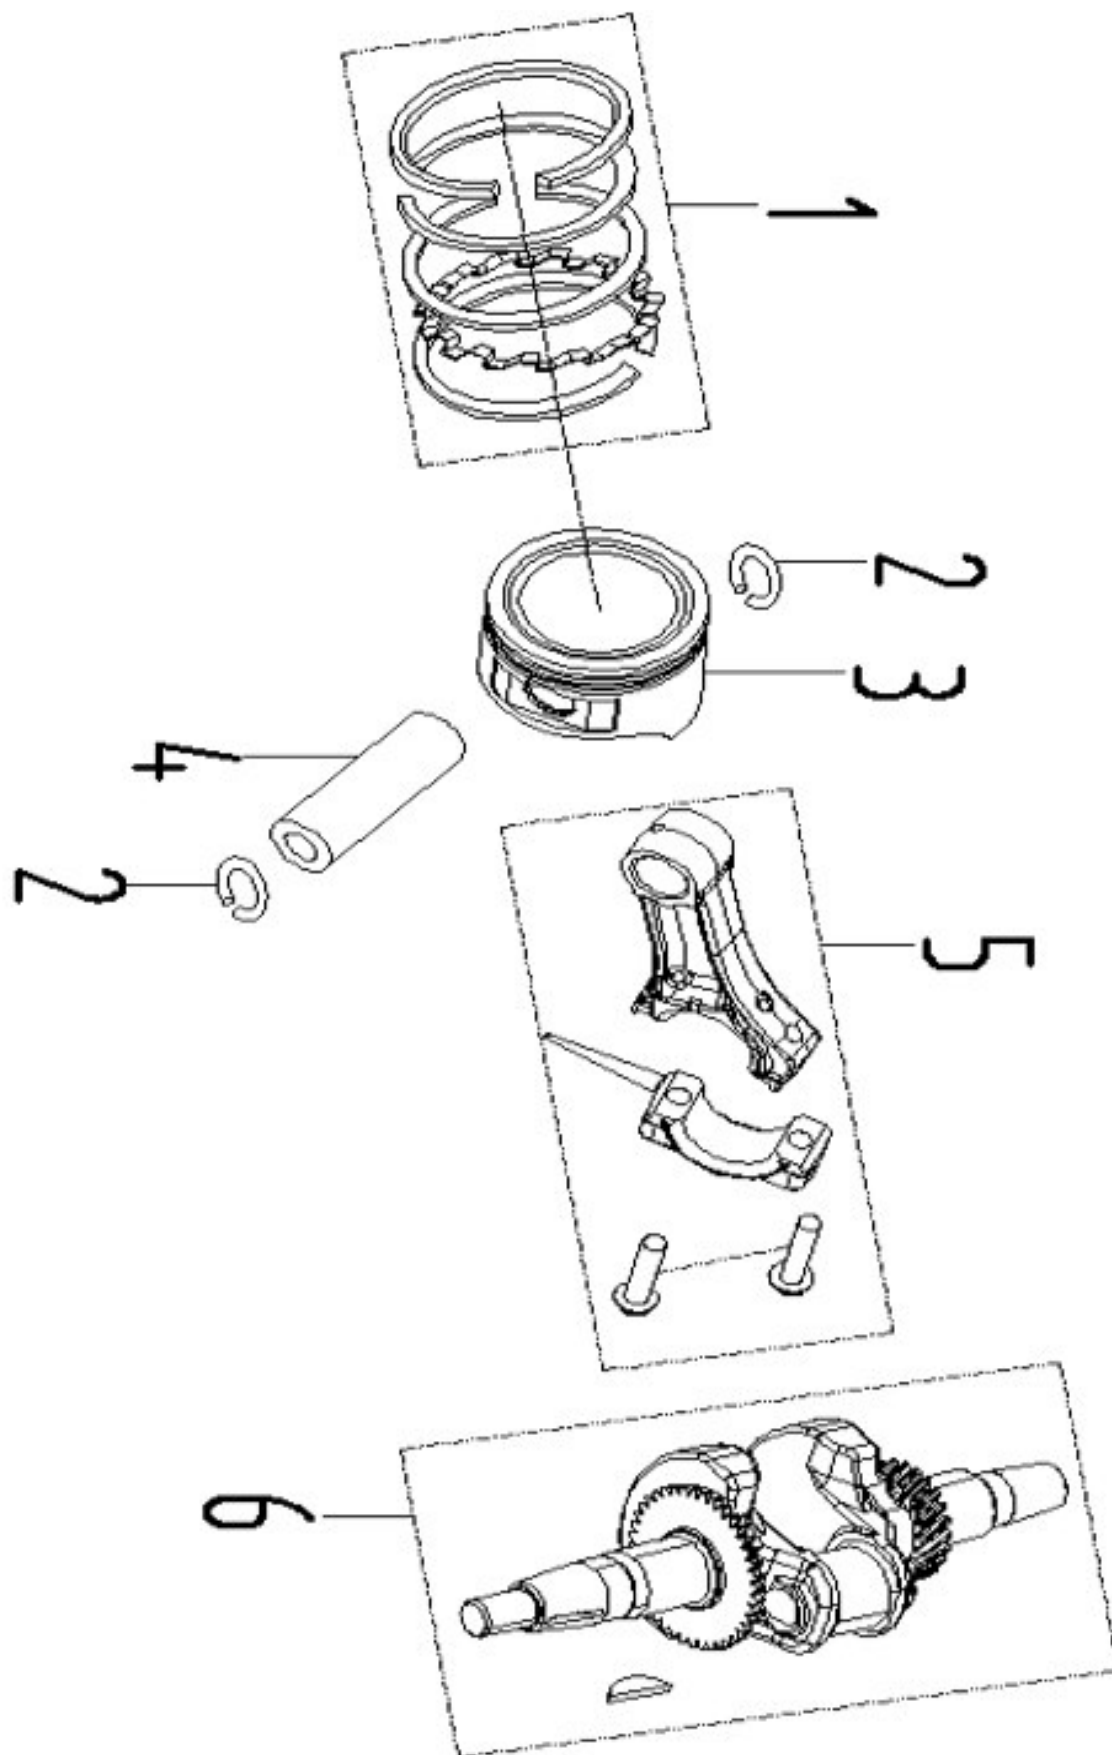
Ersatzteilzeichnung 6 - Kolben der Kurbelwelle
